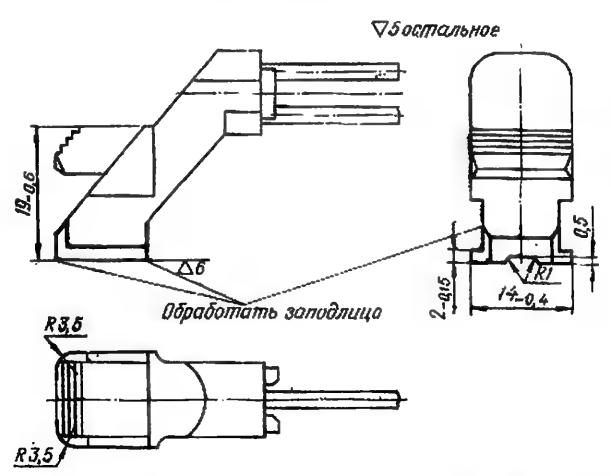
Обработка выступов пятки паправляющей возвратной пруживы после наплавки
